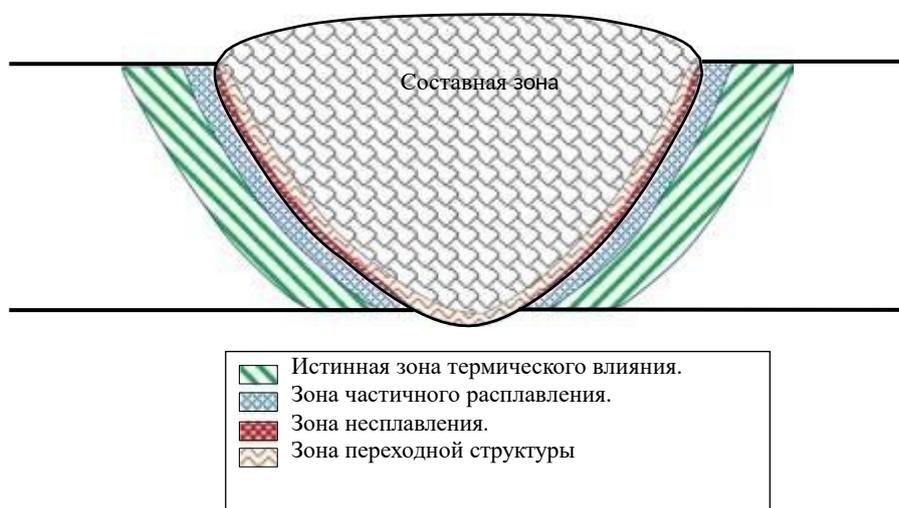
Современная схема, показывающая области шва при сварке плавлением.
